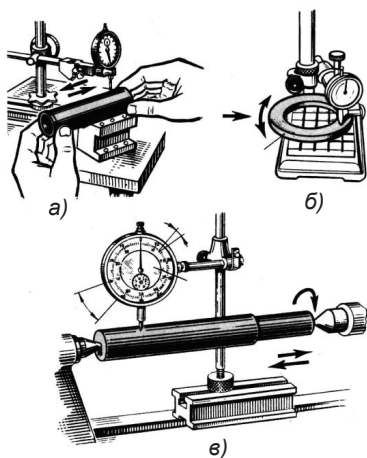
Приемы проверки индикатором: а, б) перемещением деталей; в) в центрах
